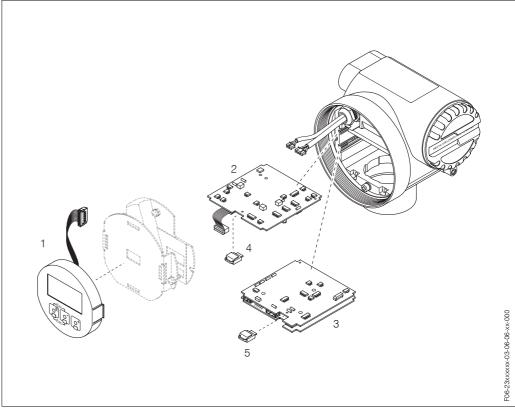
Pièces de rechange pour transmetteur Promag 23
